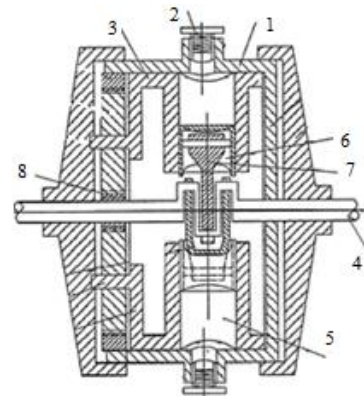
Конструктивна схема роторного двигуна барабанно-поршневого типу з рухомими камерами згоряння [3]: 1 – корпус; 2 – компресійні втулки; 3 – барабан; 4 – колінчатий вал; 5 – робочий циліндр; 6 – поршень; 7 – шатун; 8 – блок шестерень
